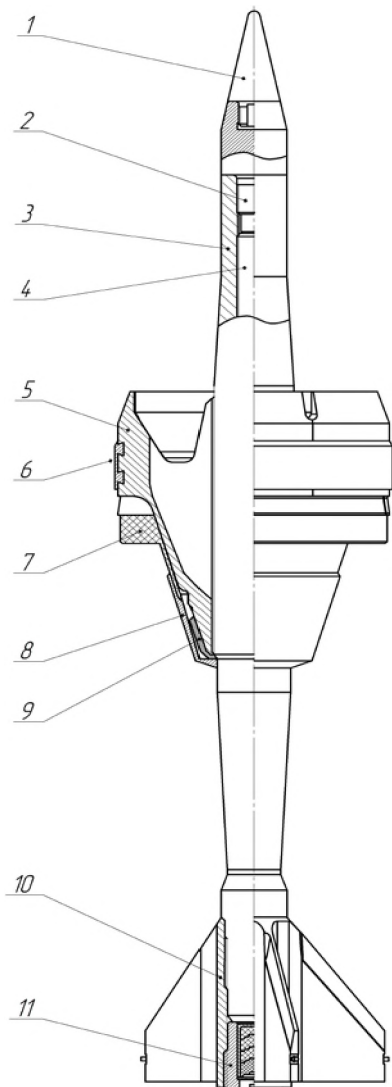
Снаряд с сердечником: 1 – баллистический наконечник; 2 – демпфер; 3 – корпус; 4 – сердечник; 5 – ведущее устройство; 6 – обтюрирующий пояс; 7 – обтюриатор; 8 – компаунд; 9 – гайка; 10 – стабилизатор; 11 – гайка трассера
